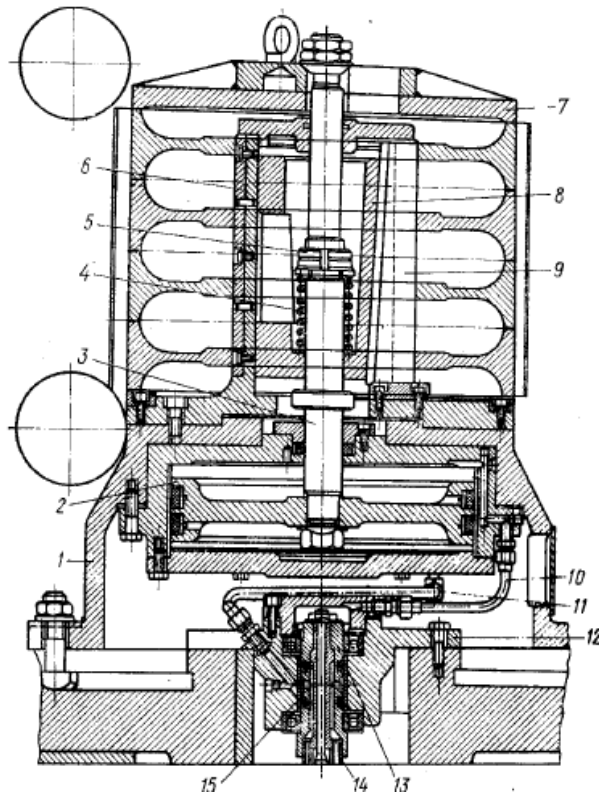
Пристосування з поршневим пневмоприводом для фрезерування зубів в декількох циліндричних колесах
